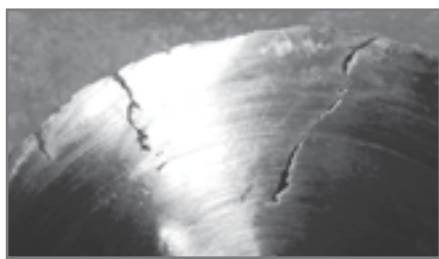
Примеры дефектов, встречающихся в заготовках
